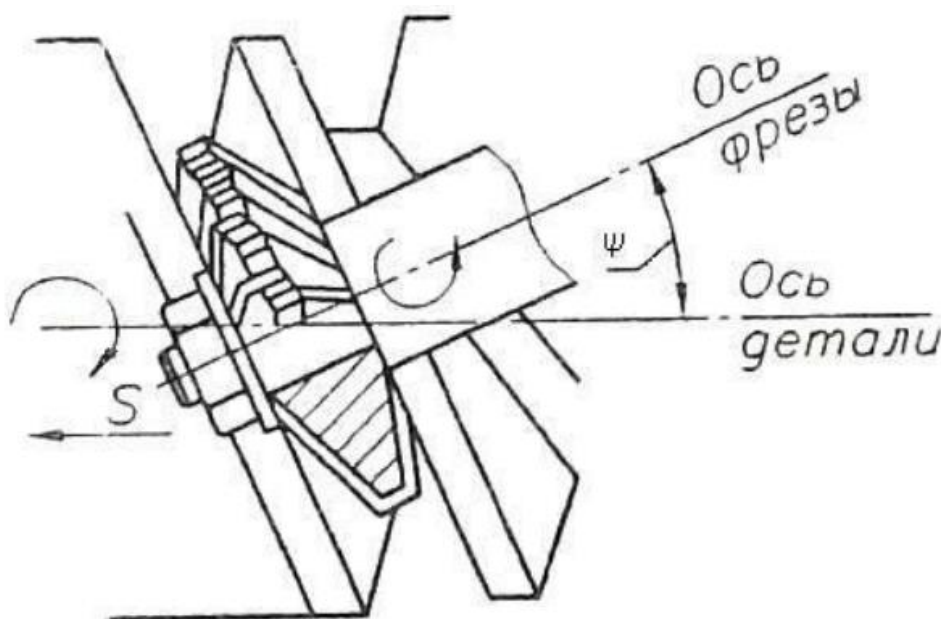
Схема установки дисковой фрезы при обработке наружных винтовых канавок
